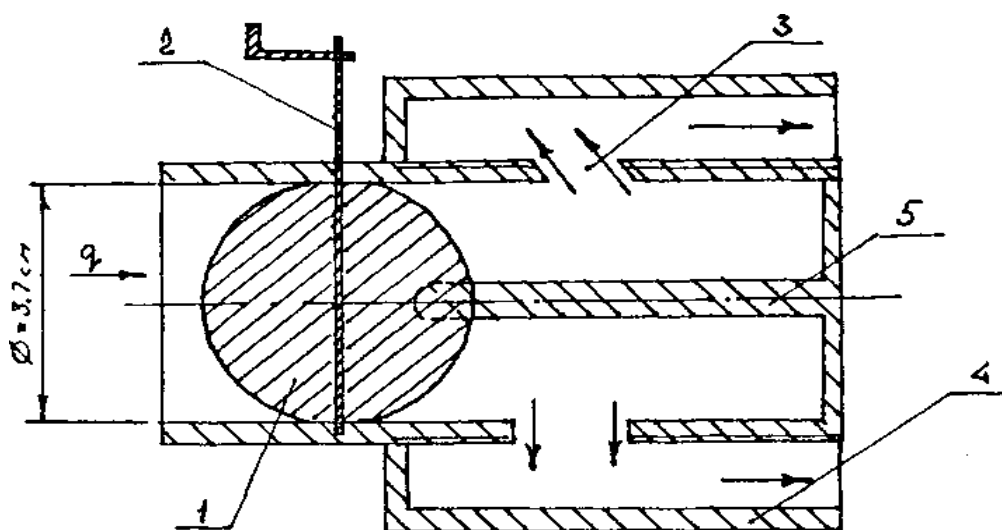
Конструкция водовыпуска поливного трубопровода: 1- поворотный клапан микрозатвора; 2 - ось вращения микрозатвора; 3-выходные отверстия водовыпуска; 4 - корпус гашения напора; 5-ограничитель поворота клапана.
